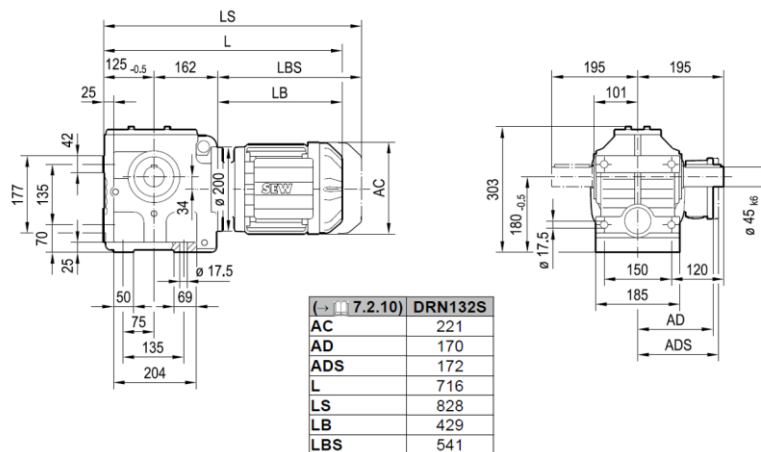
Dimensões do moto-reductor SEW S77DRN132S4 (adaptado de [22])
